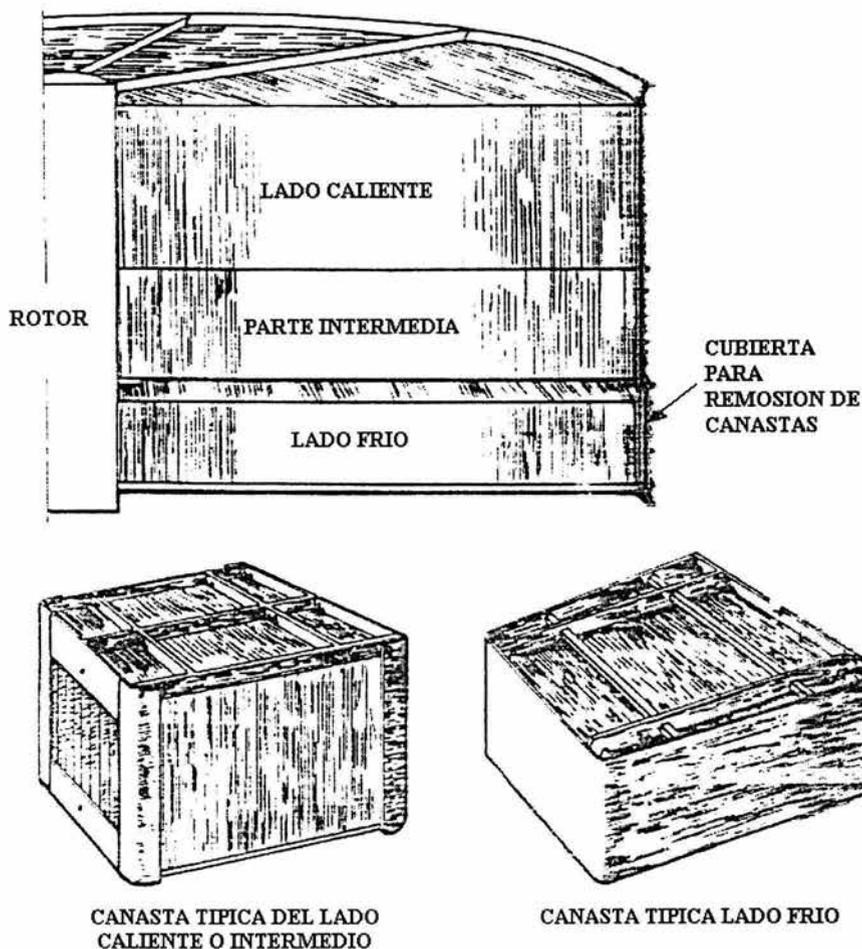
Sección del rotor mostrando la disposición de los elementos calefactores.
